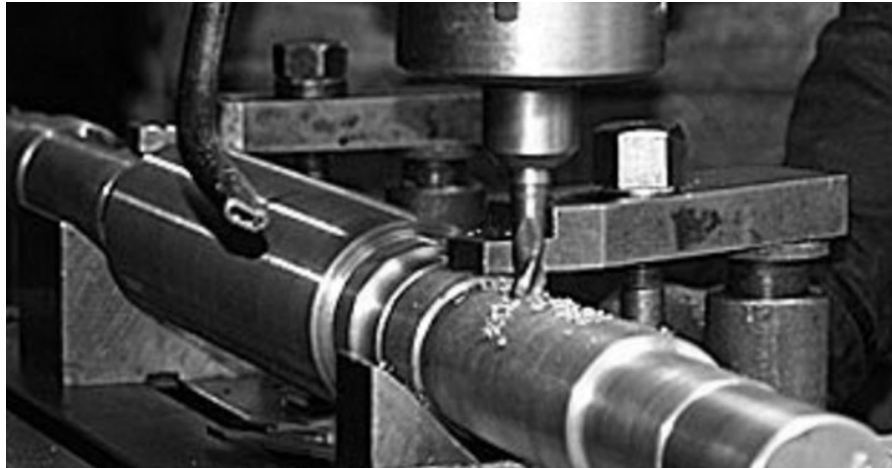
Сверление цилиндрической заготовки в призмах на сверлильном станке
